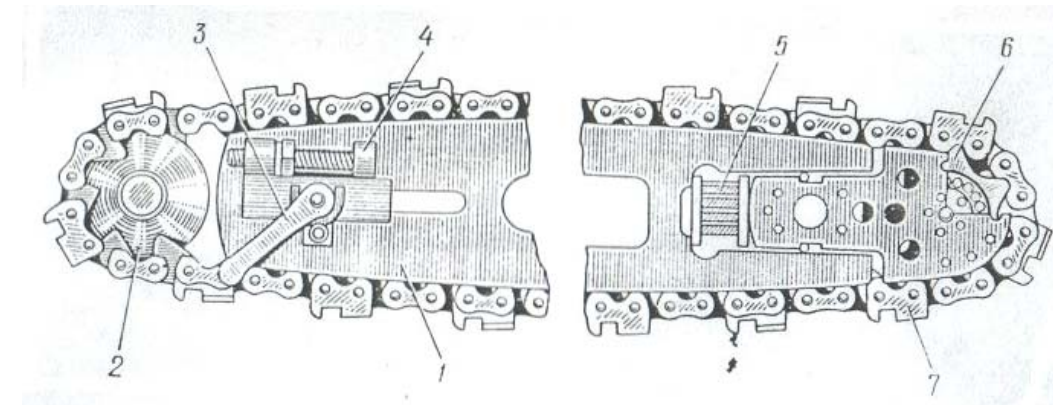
Пиляльний апарат: 1 – пиляльна шина; 2 – ведуча зірочка; 3 – пристрій для закріплення шини на упорі пилки; 4 – пристрій для натягування ланцюга на шину та зірочку; 5 – амортизатор; 6 – ведена зірочка; 7 – пиляльний ланцюг
